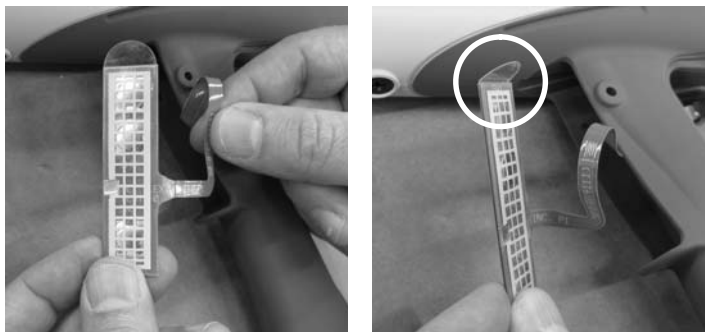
Установка выключателя спускового устройства — операция 3
